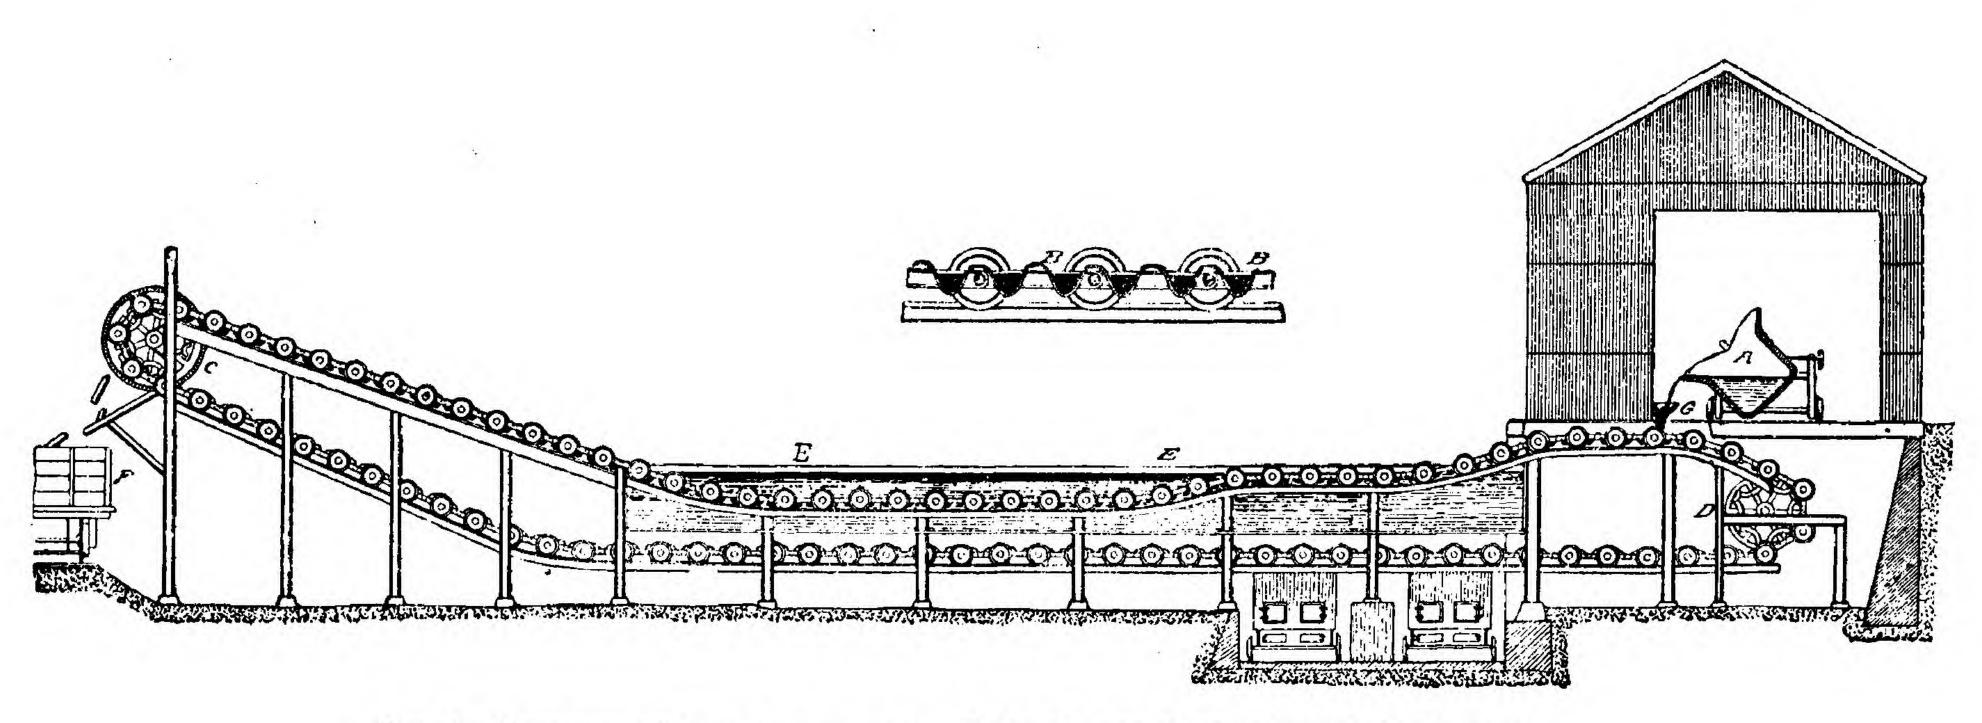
Схематическій чертежь аппарата Uehling'а для отливки чугуна въ свинки.
